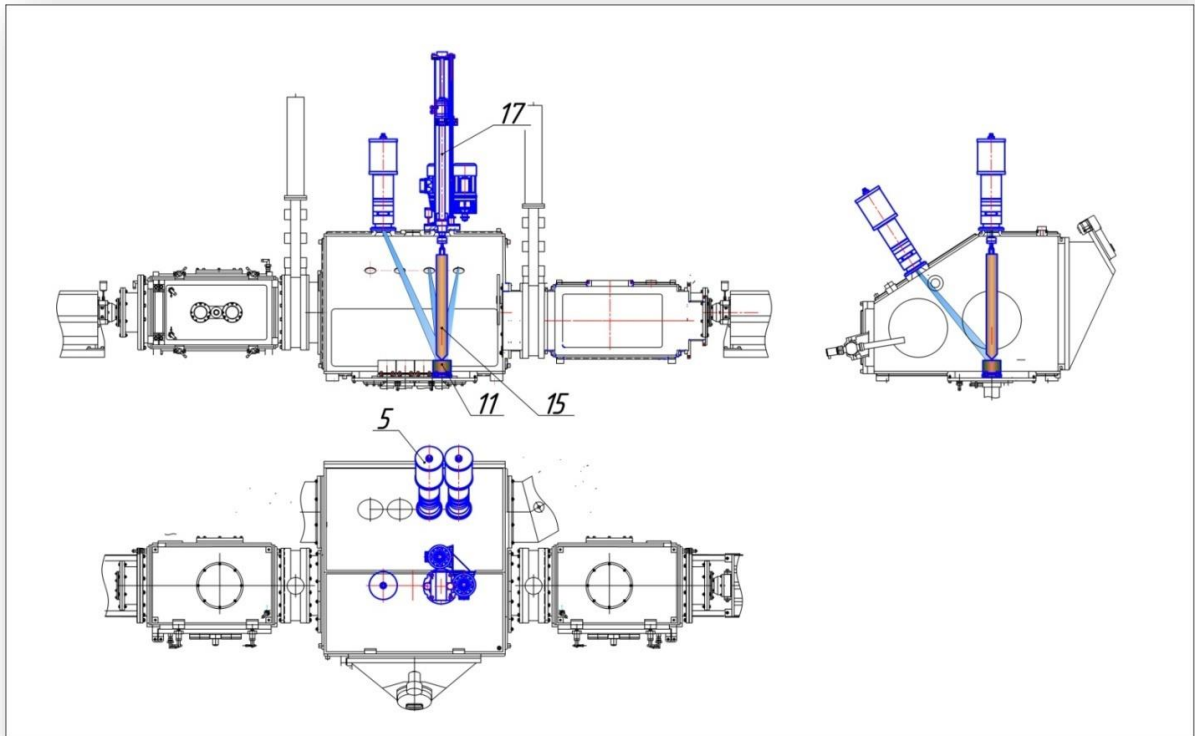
Схема переплава заготовок безпосередньо в кристалізатор (5 – електронна гармата, 11 – кристалізатор, 15 – вертикальна заготівка, 17 – механізм підвіски заготівки)
